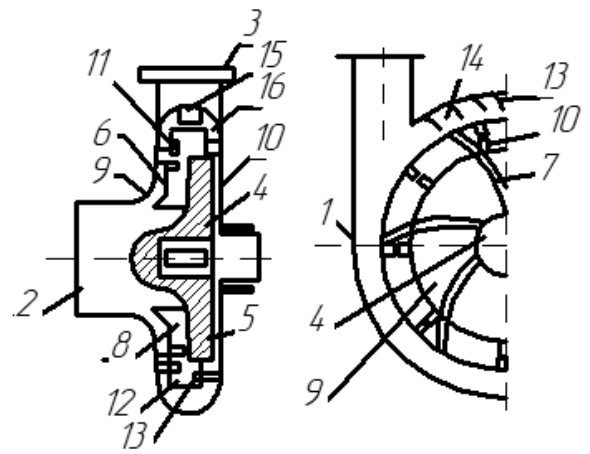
Схема і загальний вигляд роторного кавітаційного диспергатора [90]
